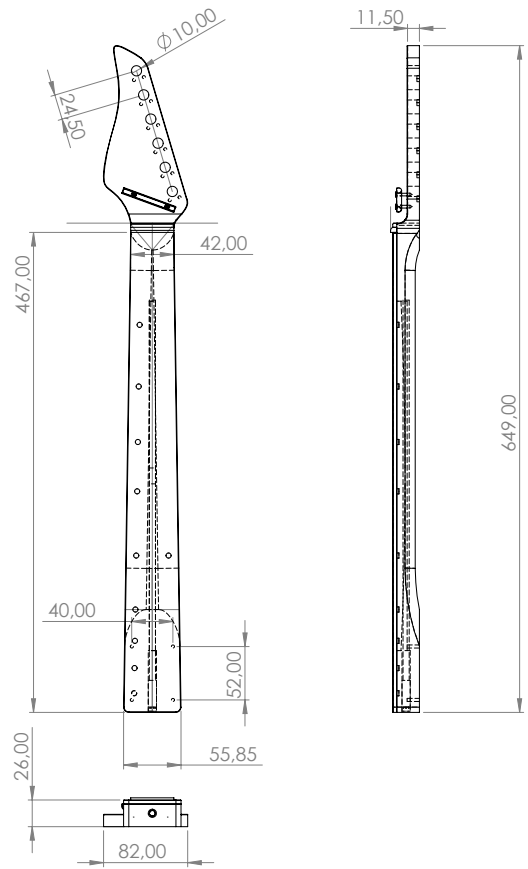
Desenho técnico - Protótipo “Braço Vidro”.
